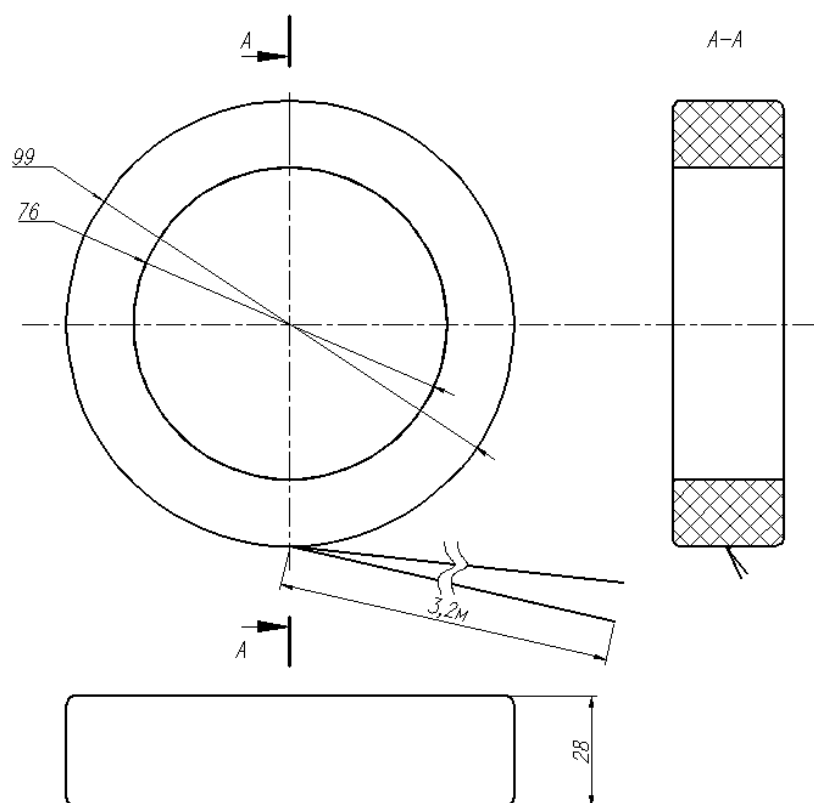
Габаритный чертеж трансформатора тока ТТ76
